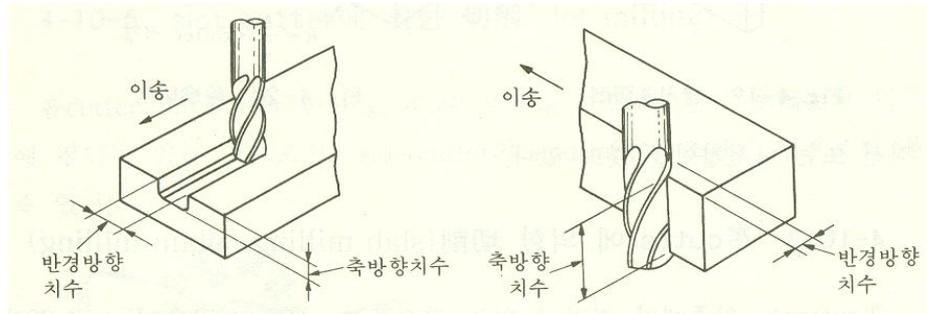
열립 홈절삭(수직 milling machine, 좌)과 원주절삭(수직 milling machine, 우)
